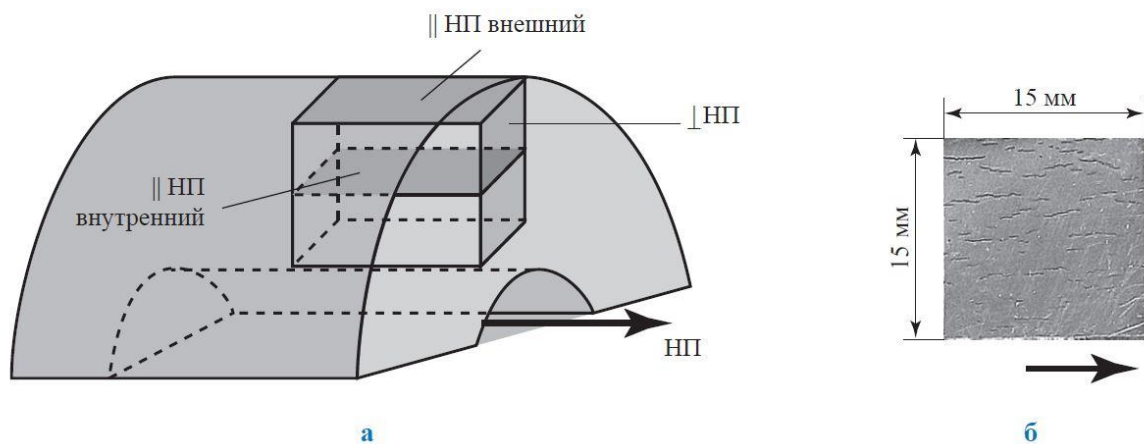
Схема вырезки (а) и внешний вид подготовленной для исследования поверхности образца ||НП (б).
